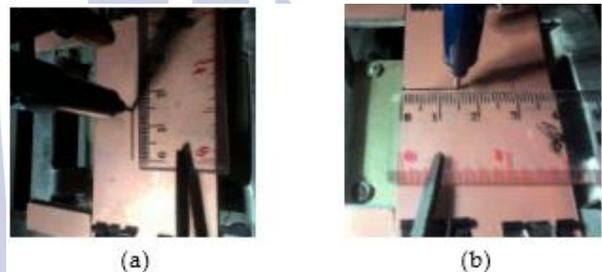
(a) Gambar tampak depan mesin pengebor PCB (b) Gambar tampak belakang mesin pengebor PCB.
